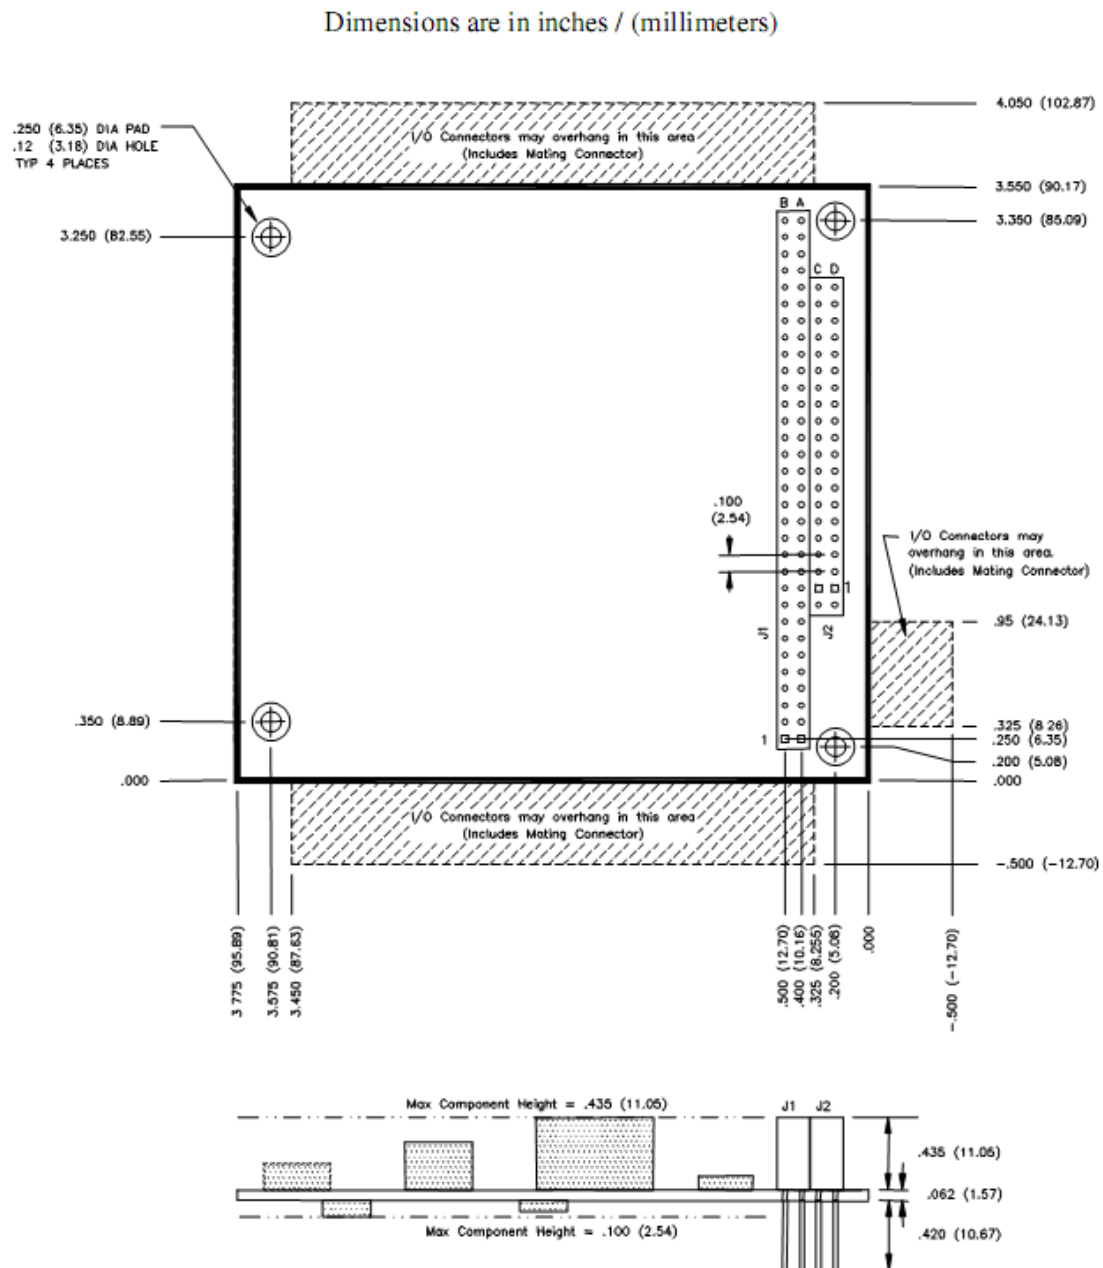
Dimensions del mòdul PC/104 16 bits
